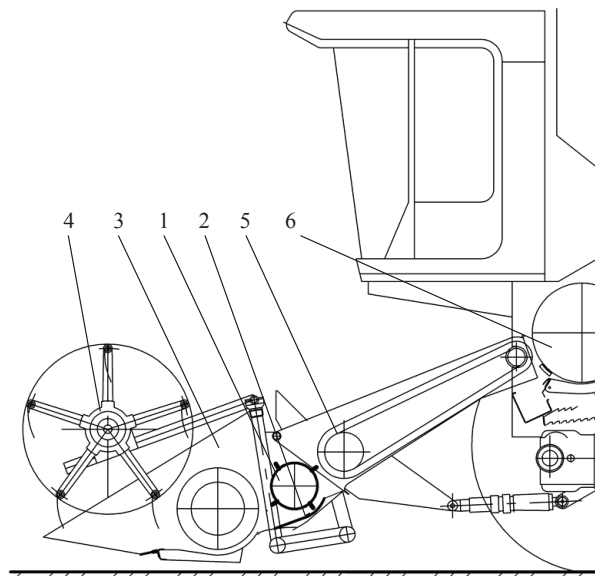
Схема загального вигляду жниварки комбайна з пристроєм попереднього обмолоту зерна: 1 – зубчато-лопатевий молотильний барабан; 2 – дека; 3 – жниварка; 4 – мотовило; 5 – транспортер похилої камери; 6 – МСС комбайна
